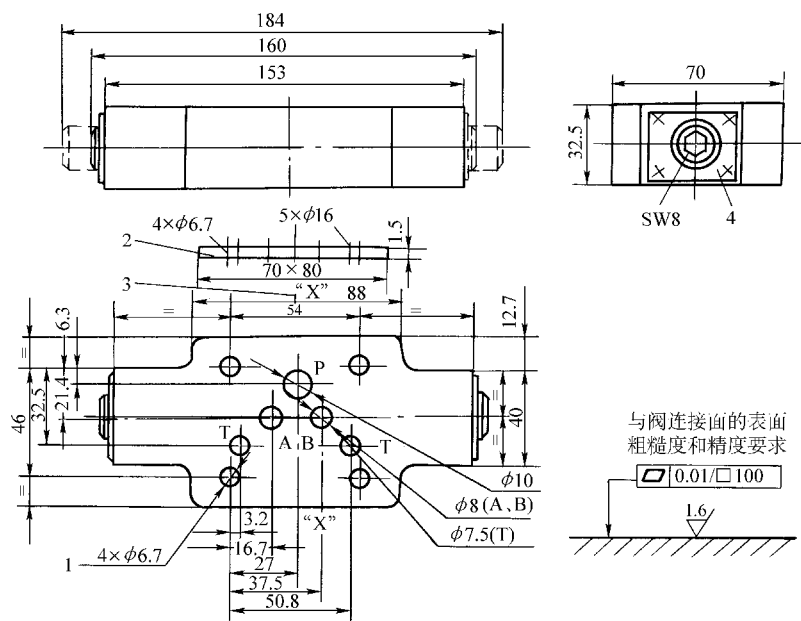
Z2FS10 型叠加式节流阀的外形尺寸
